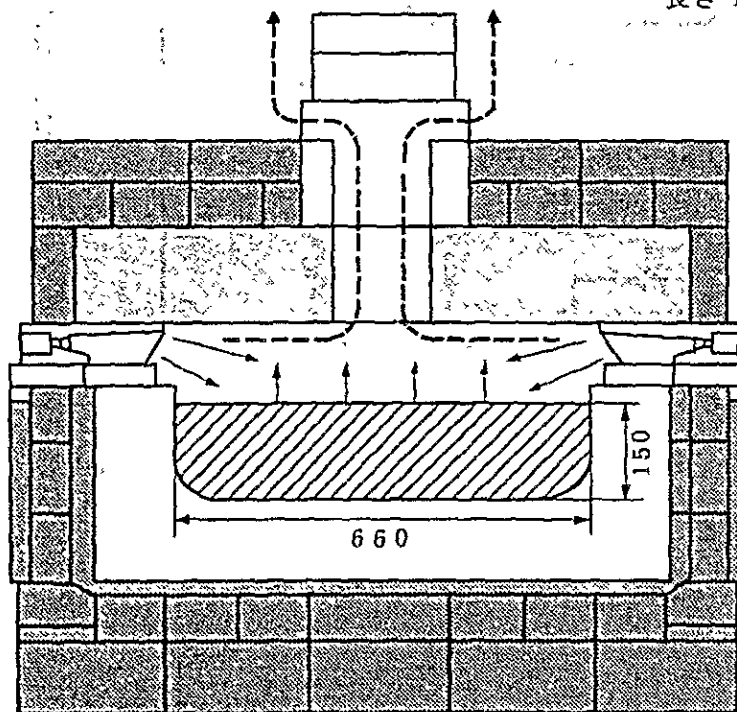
2F-1のフォアハース断面図(エムハートKWタイプ)
